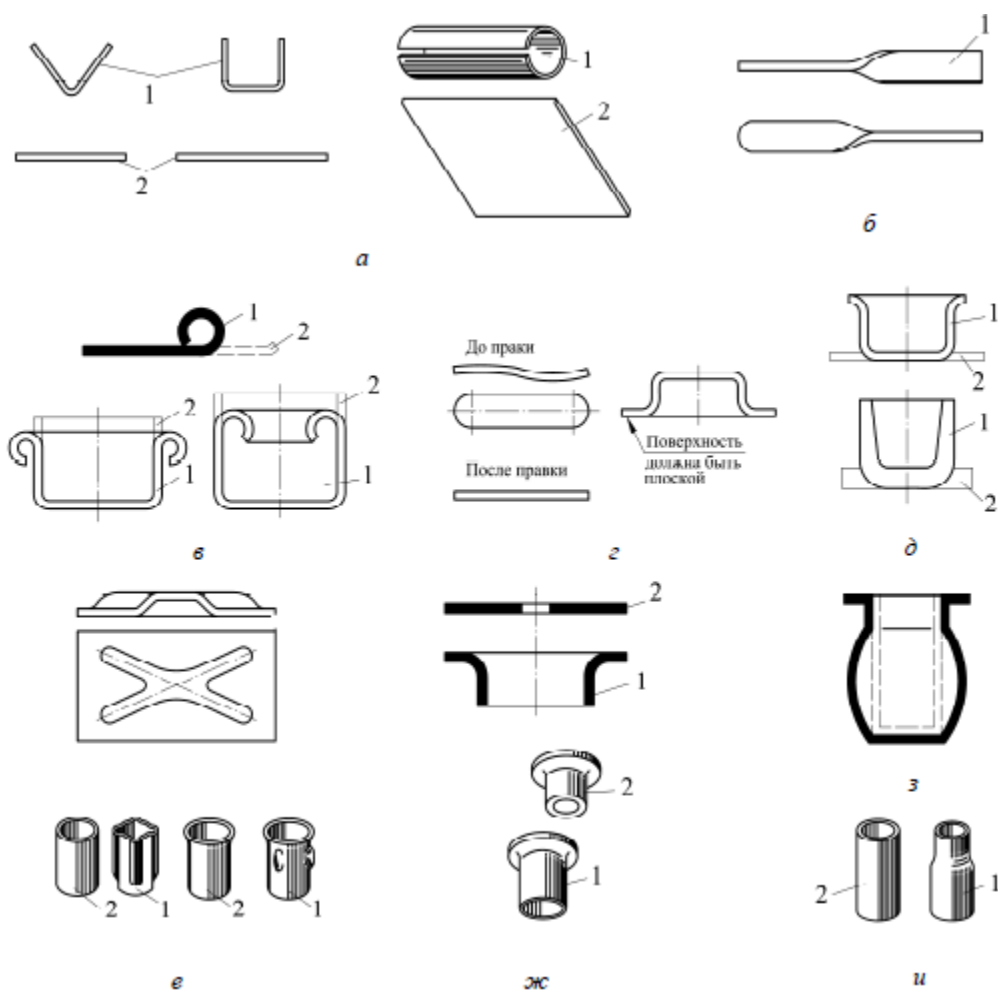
Деталь (1) и исходная заготовка (2), полученная формоизменяющей операцией листовой штамповки: а – гибкой; б – скручиванием; в – закаткой; г – правкой; д – вытяжкой; е – рельефной формовкой; ж – отбортовкой; з – раздачей; и – обжимом в штампе
